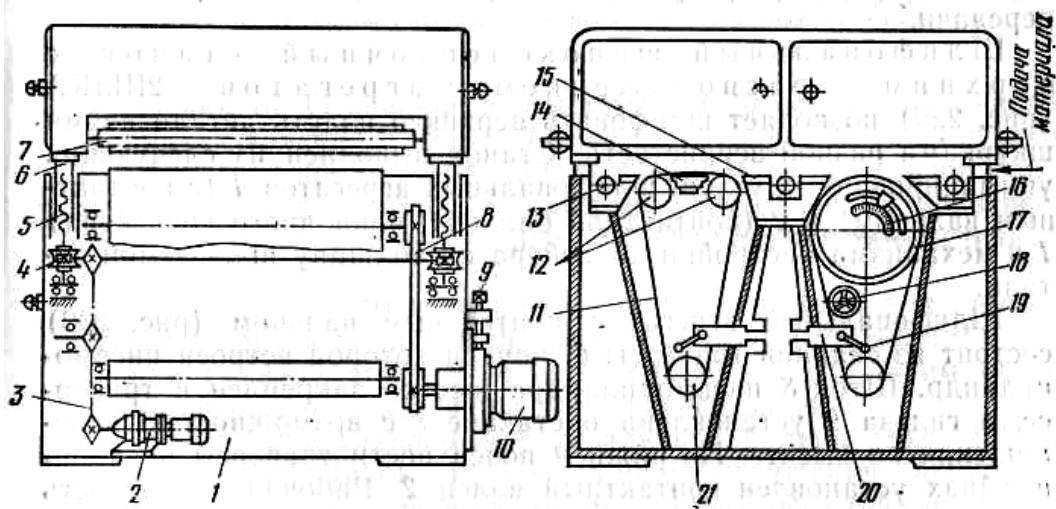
Схема широколенточного станка с нижним расположением шлифовальных агрегатов 2ШЛКН: 1 — станина, 2 — мотор-редуктор, 3 — цепная передача, 4 — червячная передача, 5 — ходовой винт, 6 — круглая направляющая, 7 — конвейер, 8 — ременная передача, 9 — регулировочный винт, 10 — электродвигатель, 11 — шлифовальная лента, 12 — поддерживающие ролики, 13 — задний ролик, 14 — контактная прижимная балка, 15 — стол, 16 — шкала, 17 — контактный валец, 18 — маховичок, 19 — рукоятка, 20 — запор, 21 — натяжной ролик
